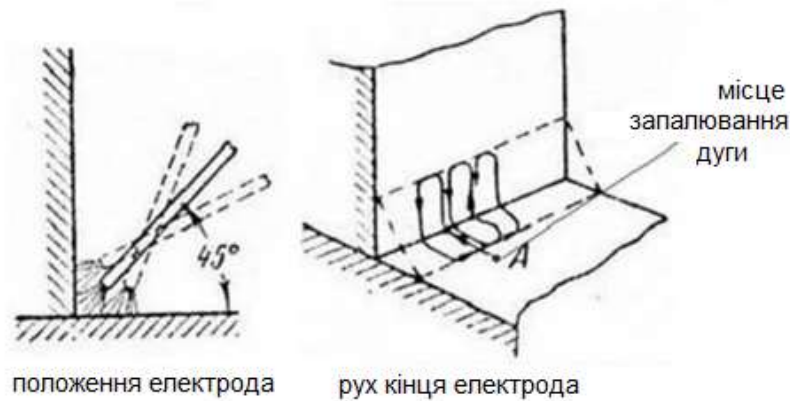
Зварювання кутового шва - положення та рух електрода
